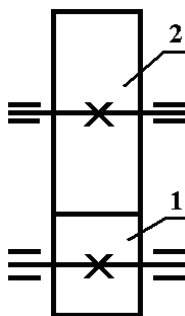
Кинематическая схема цилиндрической передачи [3]
